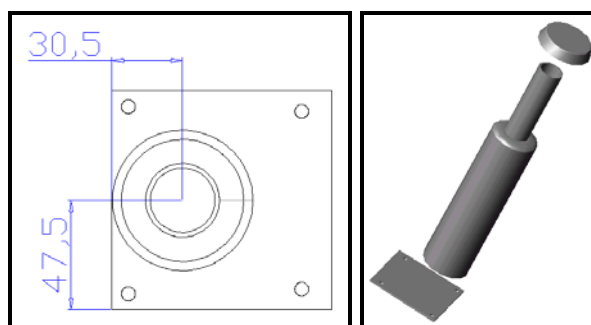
Posição de soldagem do cilindro no suporte.
